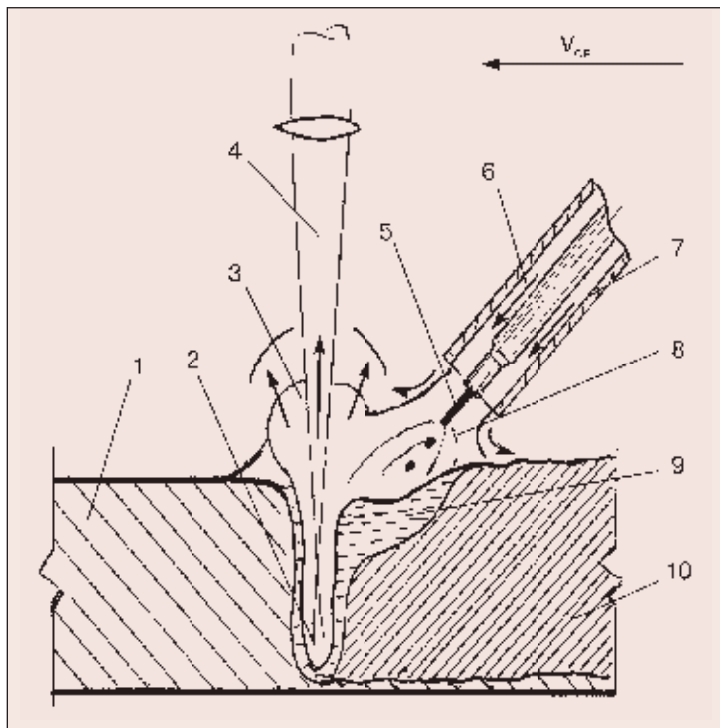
Схема лазерно-дугового (MAG) гибридного процесса: 1 — свариваемый металл; 2 — паро-газовый канал; 3 — исходящие плазма и пары металла; 4 — лазерный пучок; 5 — сварочная проволока; 6 — защитный газ; 7 — сварочная горелка; 8 — зона сварочной дуги; 9 — жидкий металл сварочной ванны; 10 — металл сварного шва
